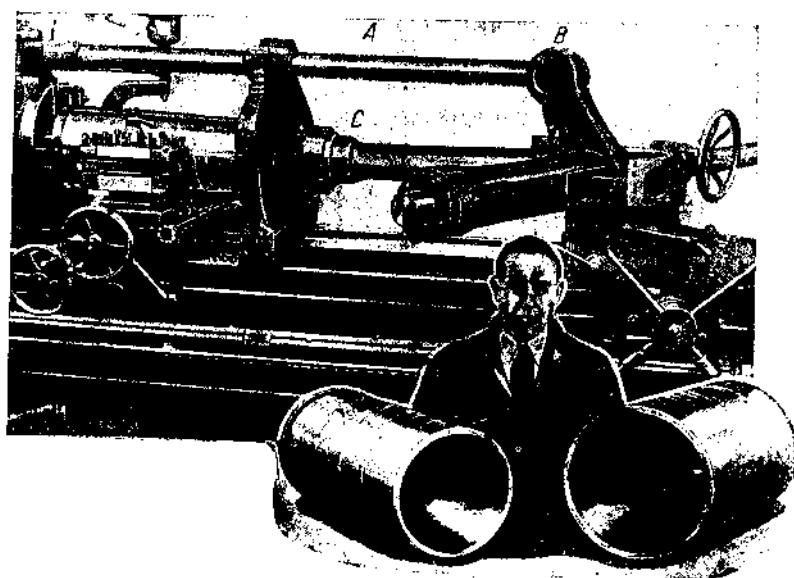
Другой набор инструмента при обработке втулки двигателя Дизеля на станке Герб
